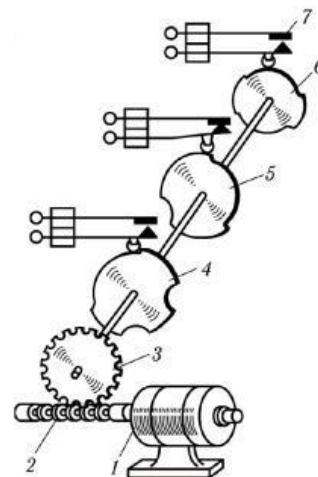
Кодовий колійний трансмітер КПТШ
